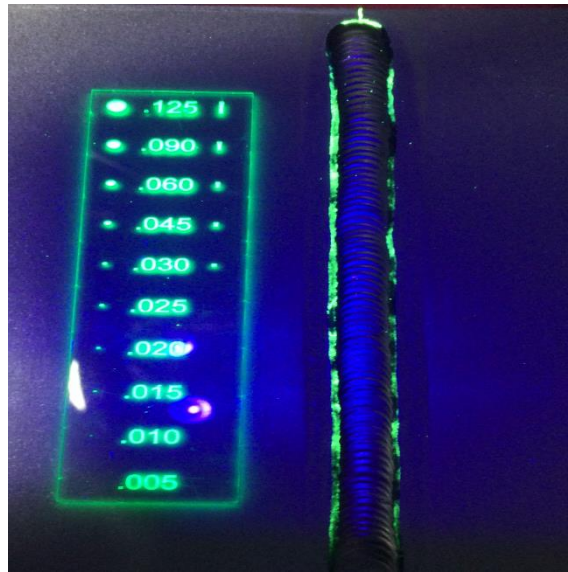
Medición con patrón de Porosidad en las Probetas de Soldadura
